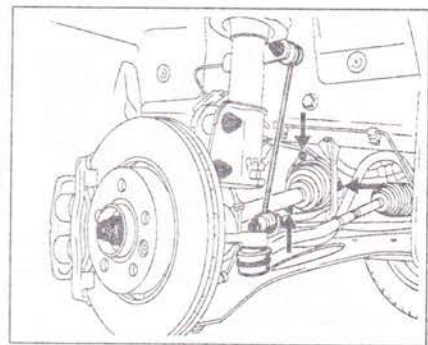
Открутите болты крепления держателя пыльника внутреннего шарнира полуоси к коробке передач.
